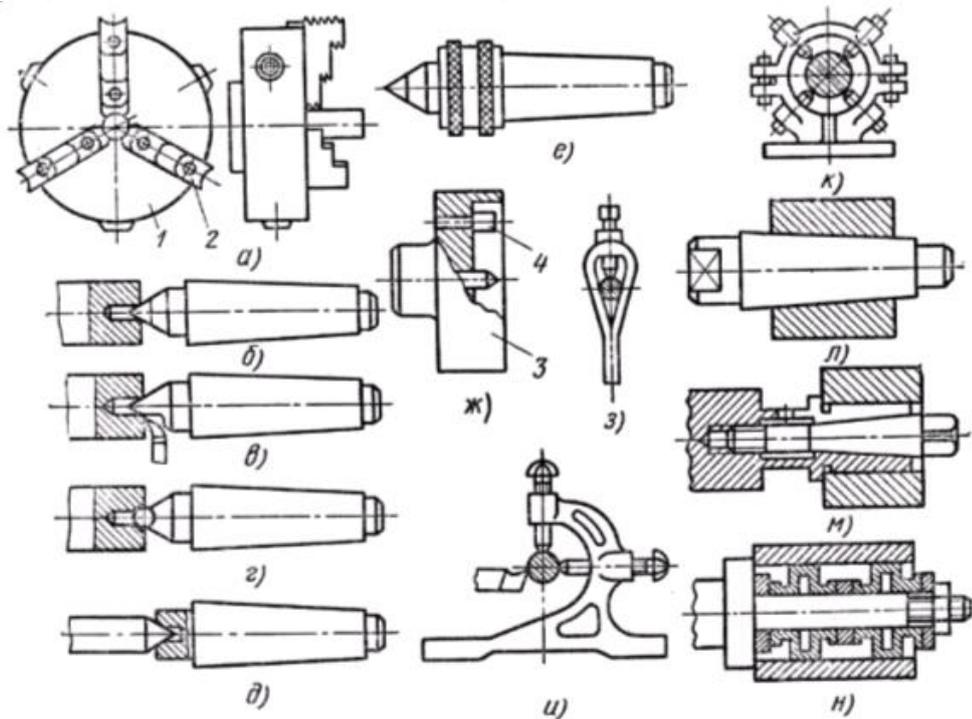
Приспособления для закрепления заготовок на токарных станках: а – патрон (самоцентрирующий или несамоецентрирующий); б – упорный центр; в – срезанный центр; г – центр со сферической рабочей частью; д, е – вращающиеся центры; ж – поводковый патрон; з – хомутик; и, к – люнеты; л – коническая оправка; м – цанговая оправка; н – упругая оправка
